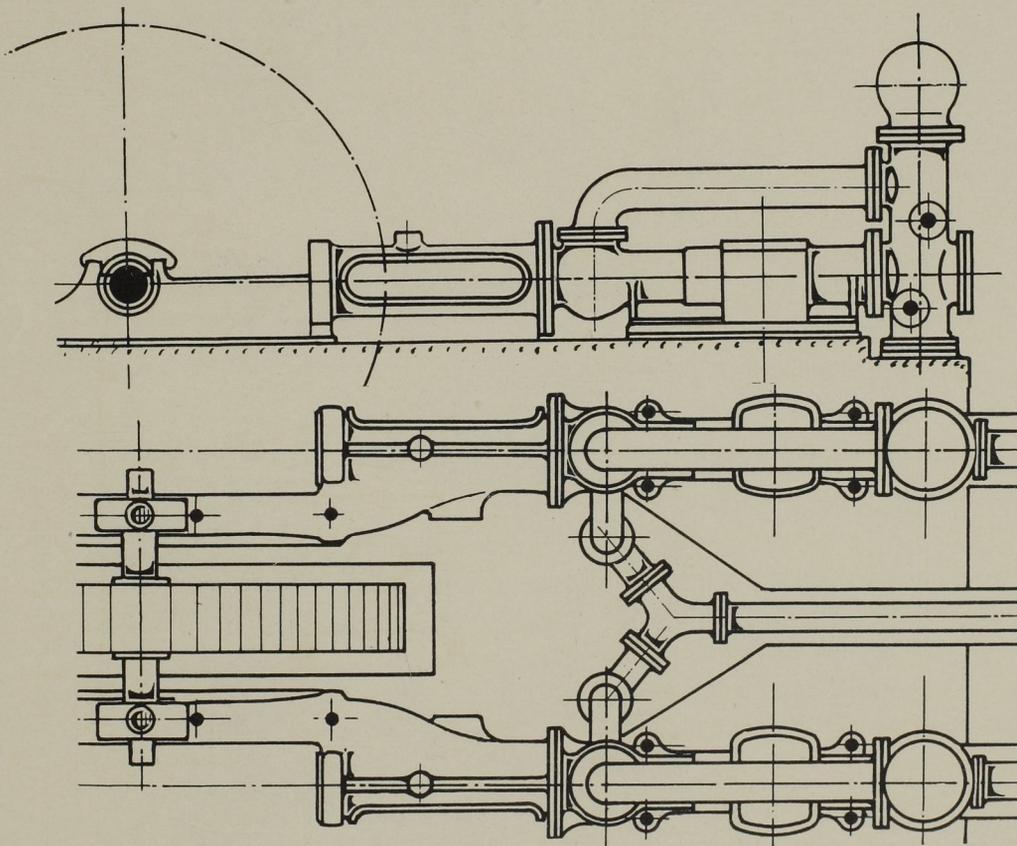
Seitenansicht und Grundriss der Pumpe. Massst. 1:40.
